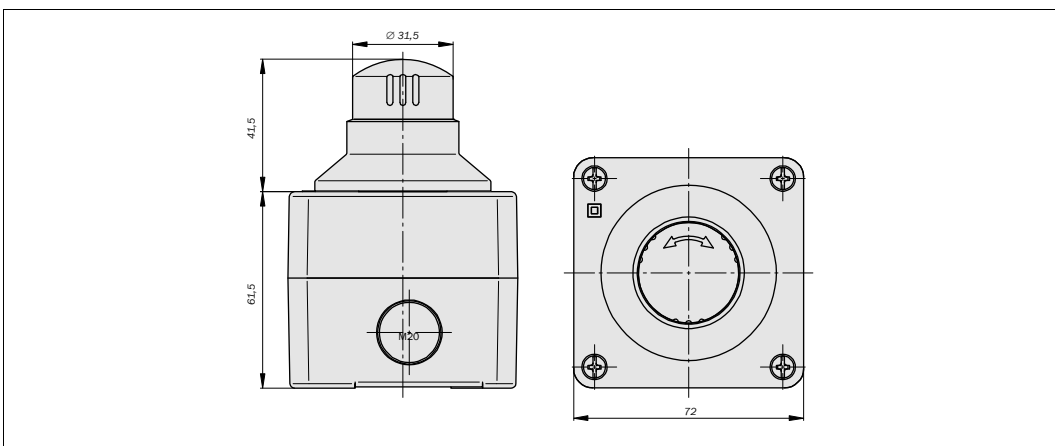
Croquis de dimensiones de la versión de montaje superficie (mm)
